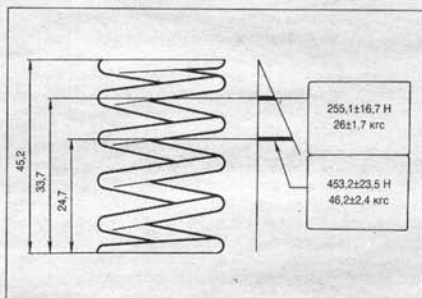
Основные данные для проверки наружной пружины клапана
